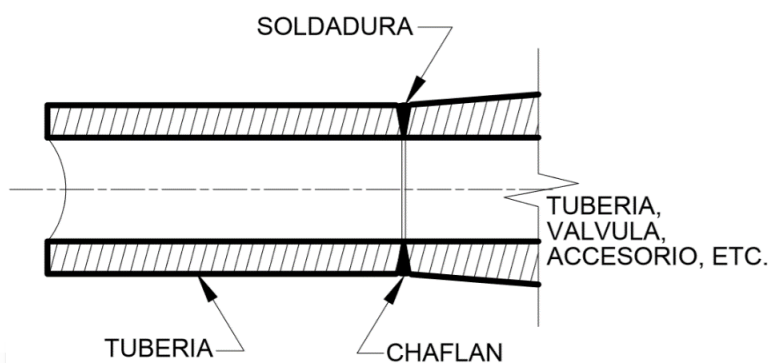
Soldadura a tope, adaptada de Rodabaugh [9]
